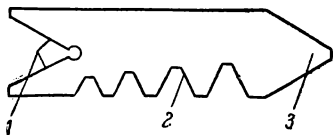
Шаблон для контроля профиля при заточке резьбовых резцов.
